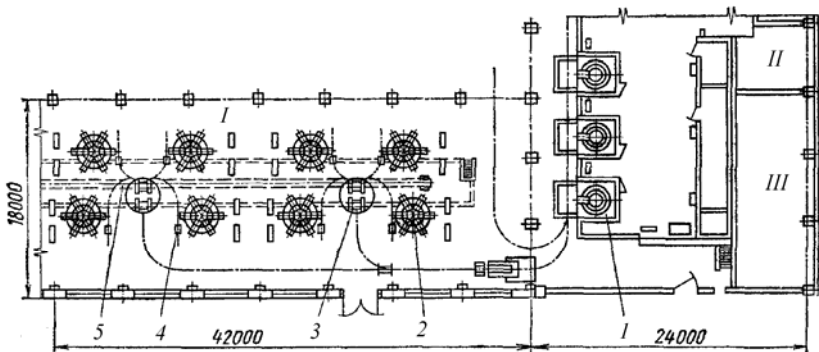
Комплексно-механізована лінія з карусельними машинами для лиття в металеві форми:
